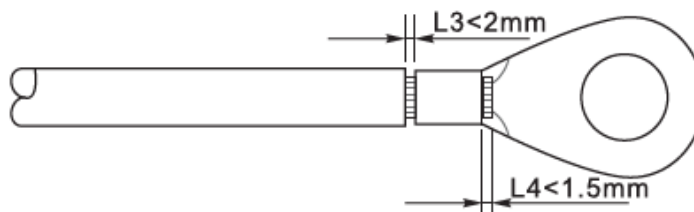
Przygotowanie przewodu uziemienia (1)
